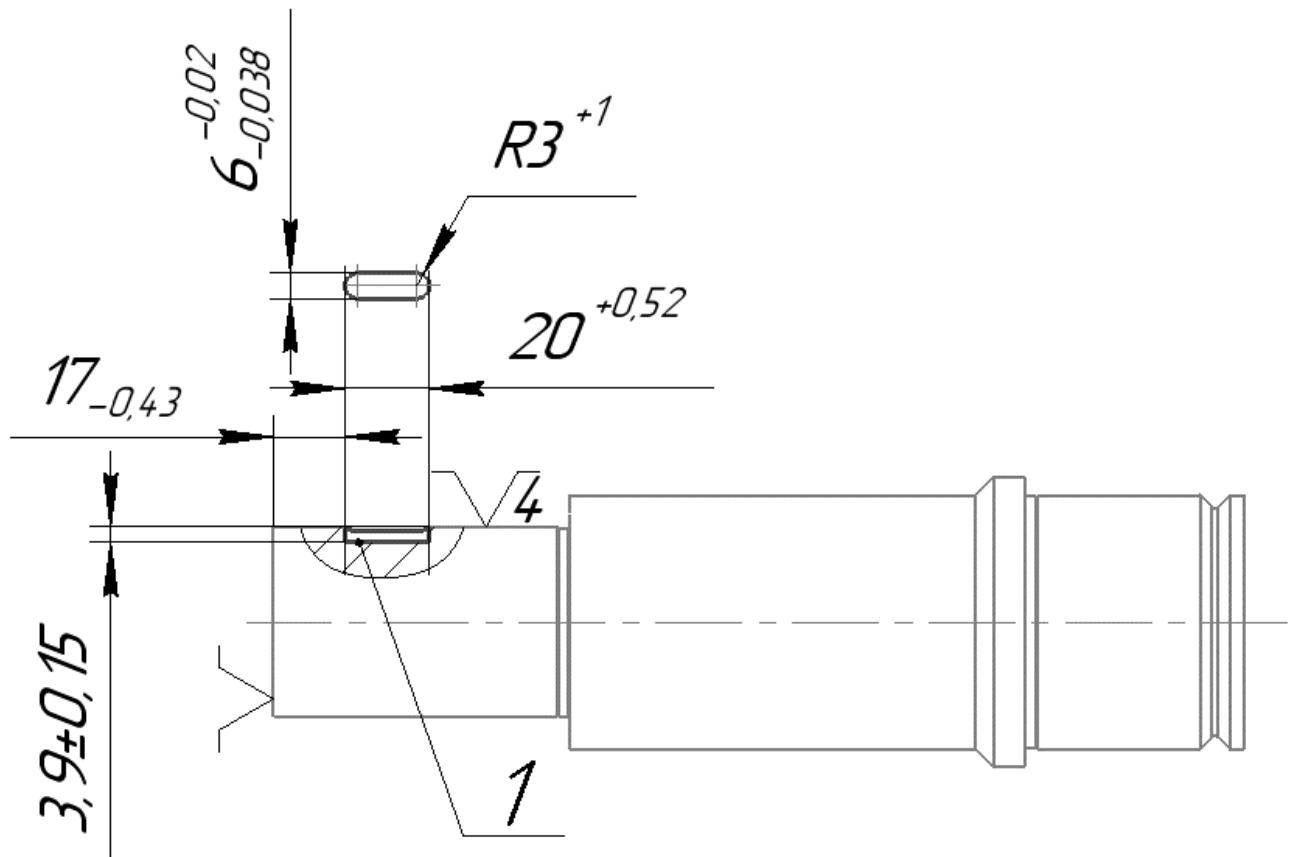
Эскиз операции 030 Фрезерная с ЧПУ (Установ А)
